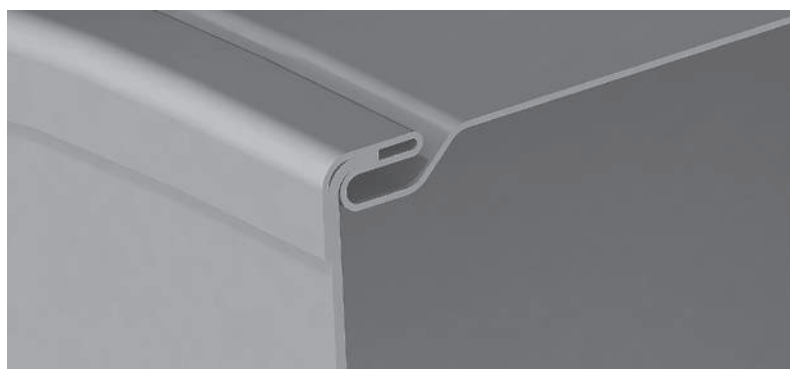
Сборка корпуса вентилятора на «питтсбургском фальце»
